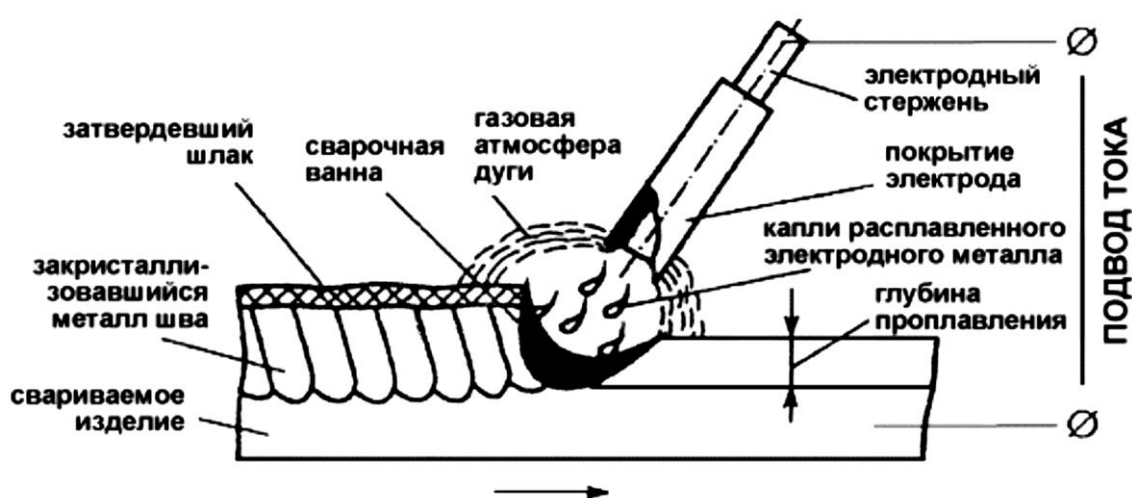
Схема дуговой сварки штучными электродами
